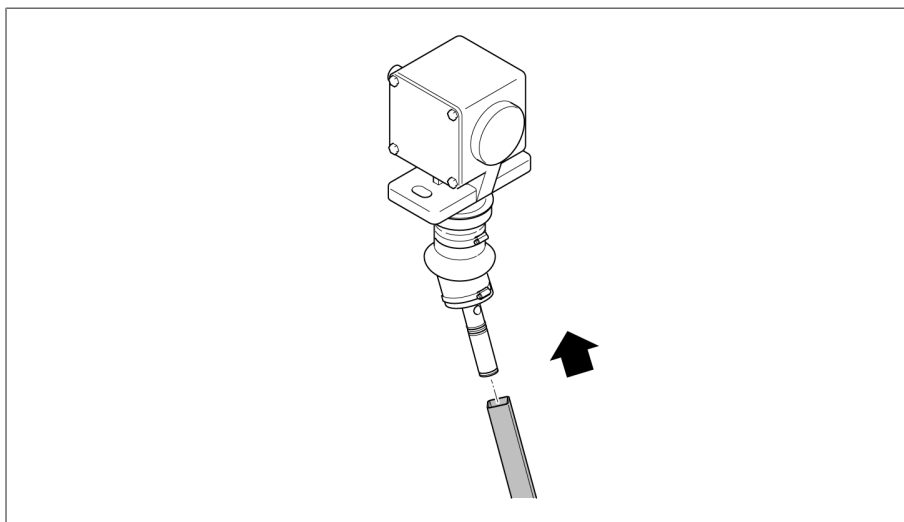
Glisser le tube carré par-dessus l'extrémité de cardan supérieure
